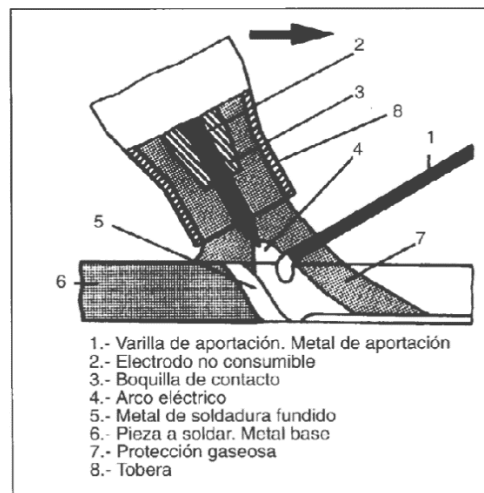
Esquema dels elements que intervenen en una soldadura TIG. Apunts Tecnologia Mecànica.
